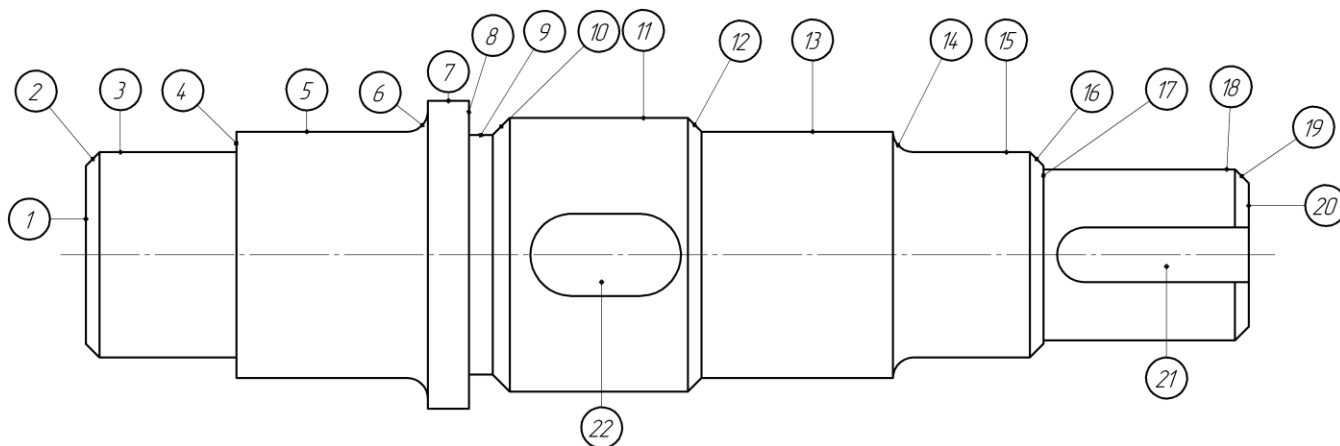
Ескіз деталі з номерами поверхонь
